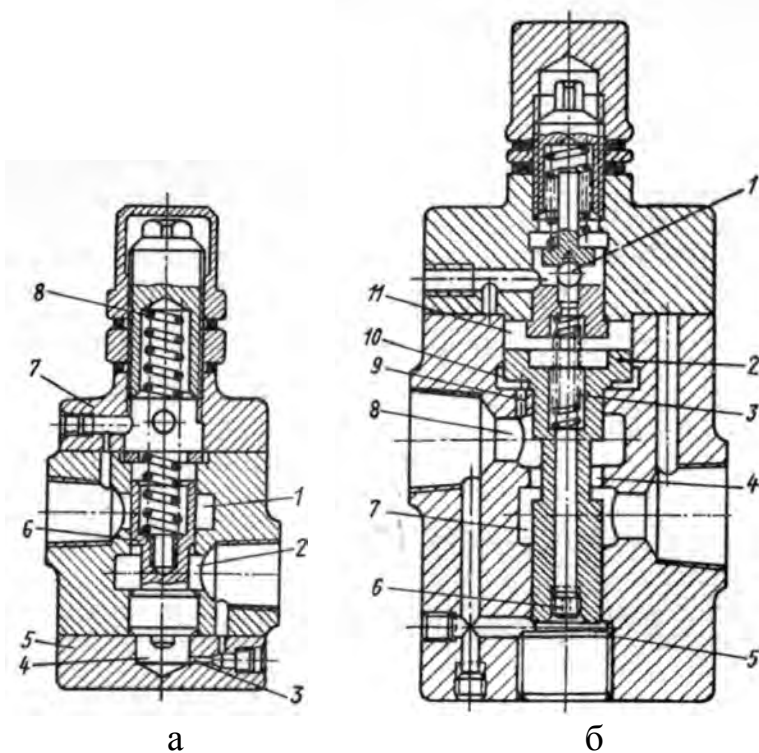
Напорный золотник (а) и редукционный клапан (б)
